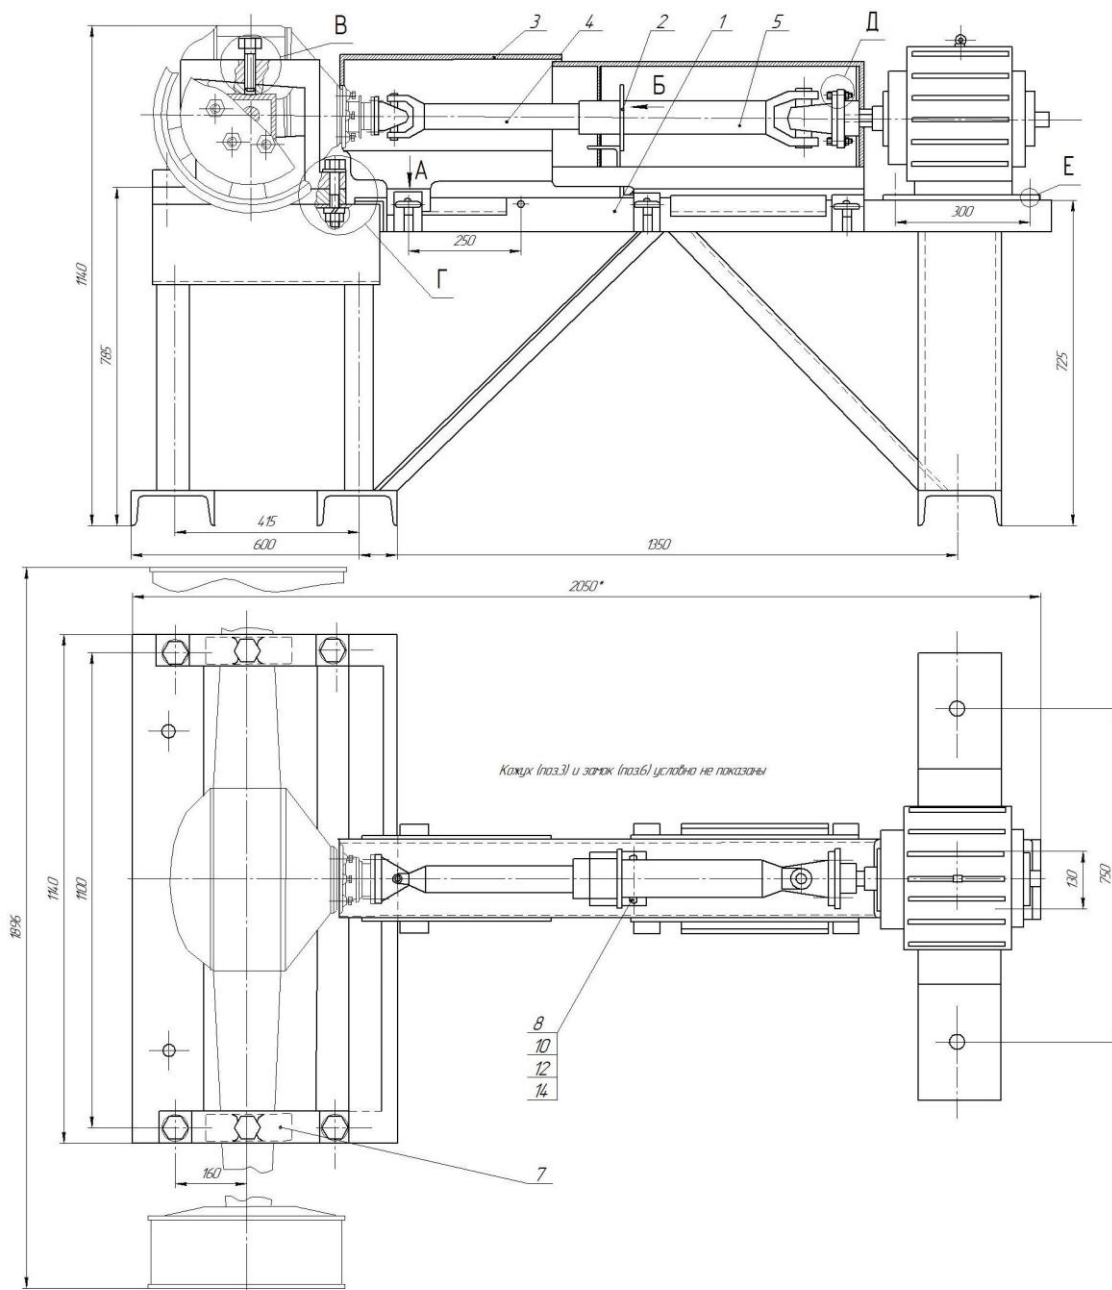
Стенд для испытания главной передачи автомобиля ГАЗель NEXT
